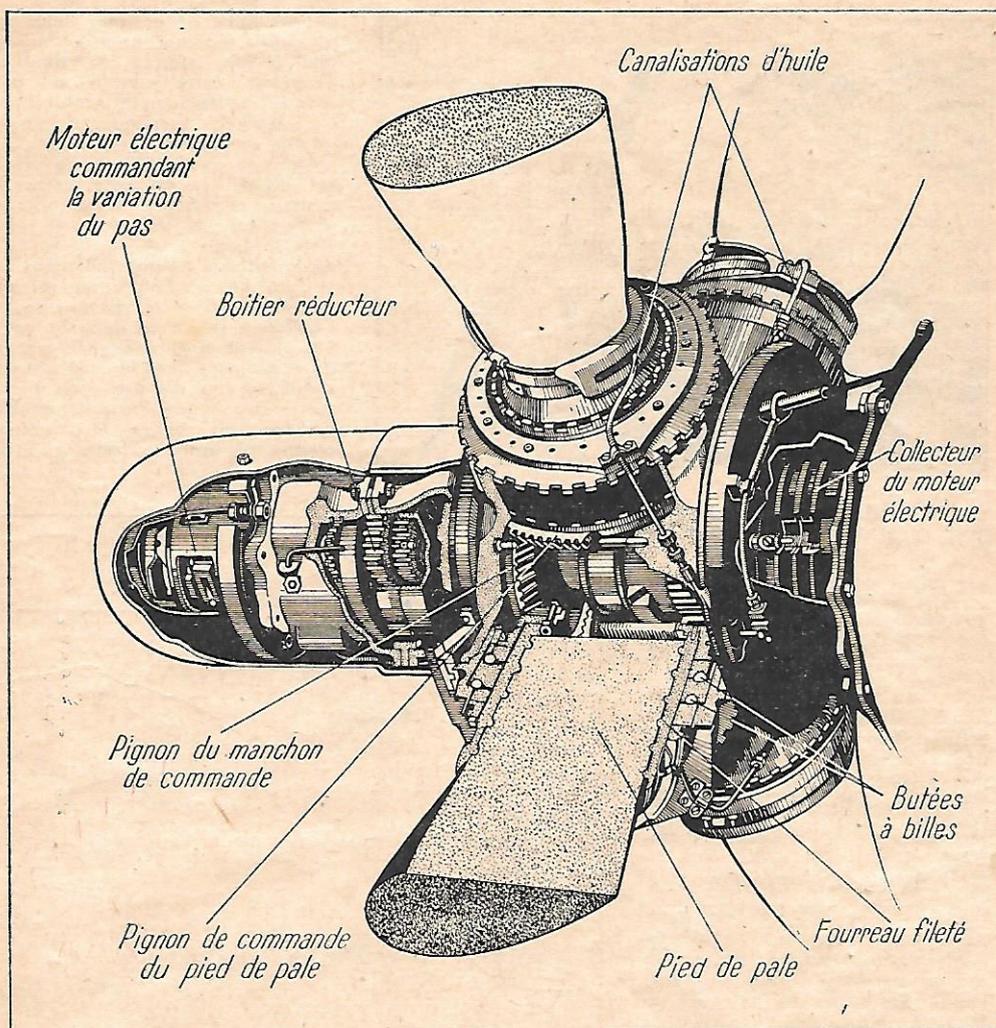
COUPE DU MOYEU D'UNE HÉLICE ROTOL ÉLECTRIQUE QUADRIPALE
